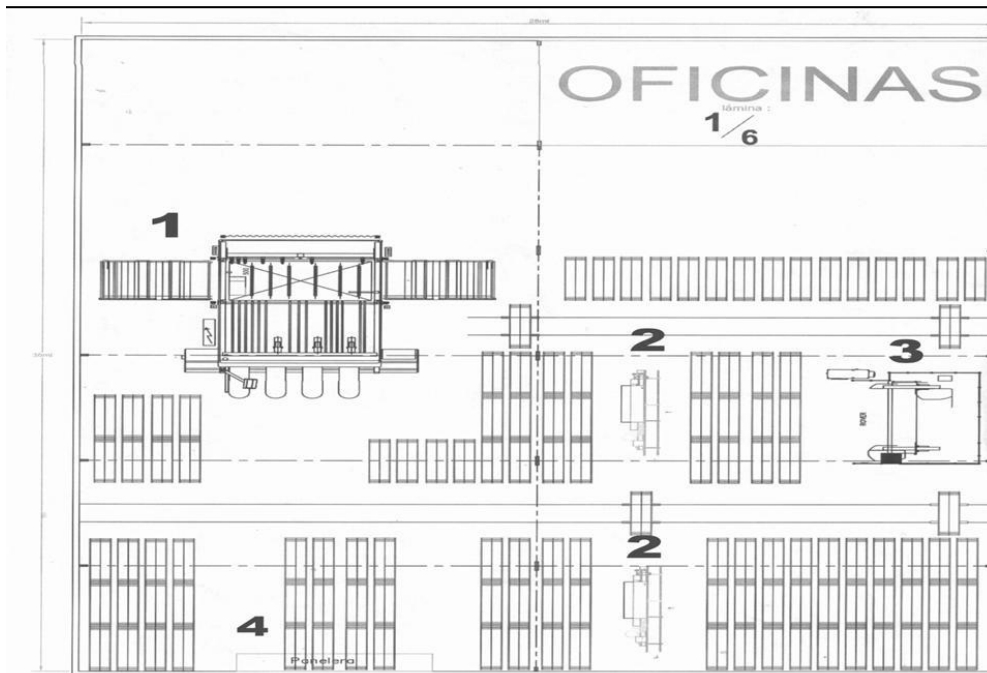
"LAYOUT de Planta Industrial PRODEMAC"
